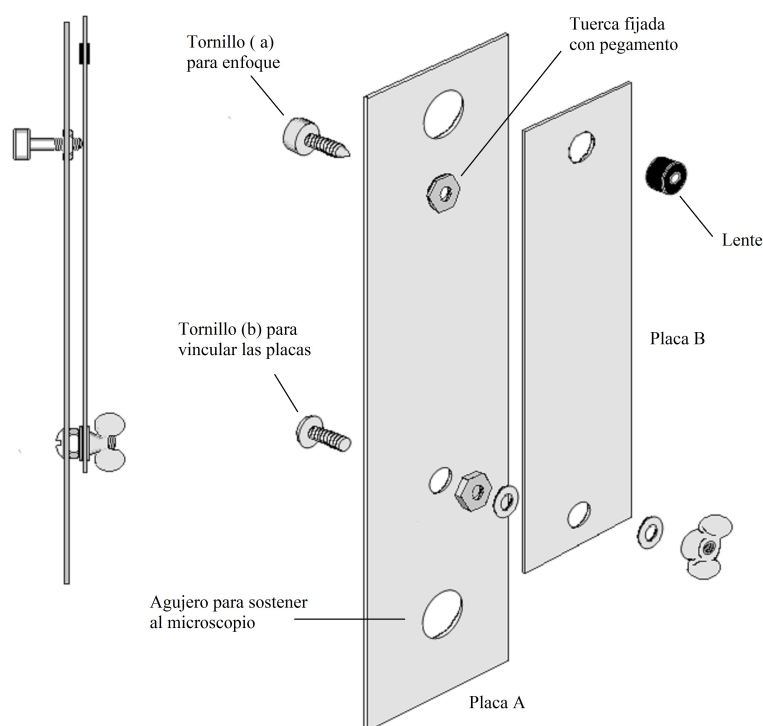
Vista de perfil y detalle de los componentes y su montaje.
